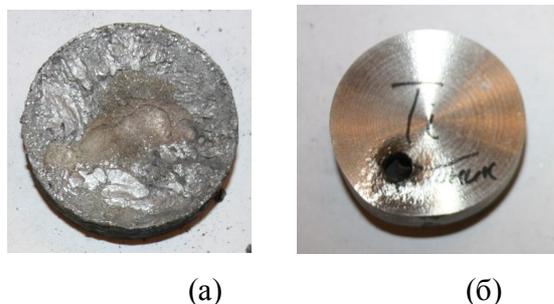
Внешний вид образцов после испытания: а) однослойный материал основы (пробой), б) двухслойный композит.
